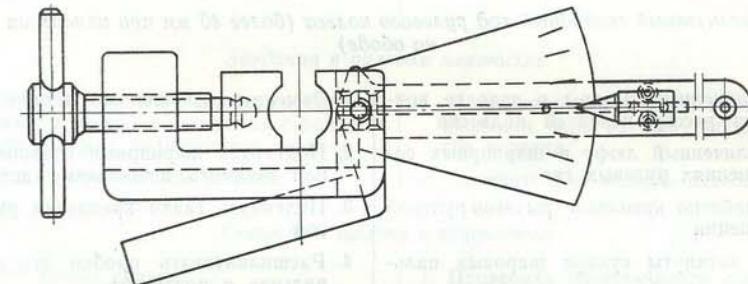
Приспособление для проверки затяжки подшипников червяка
